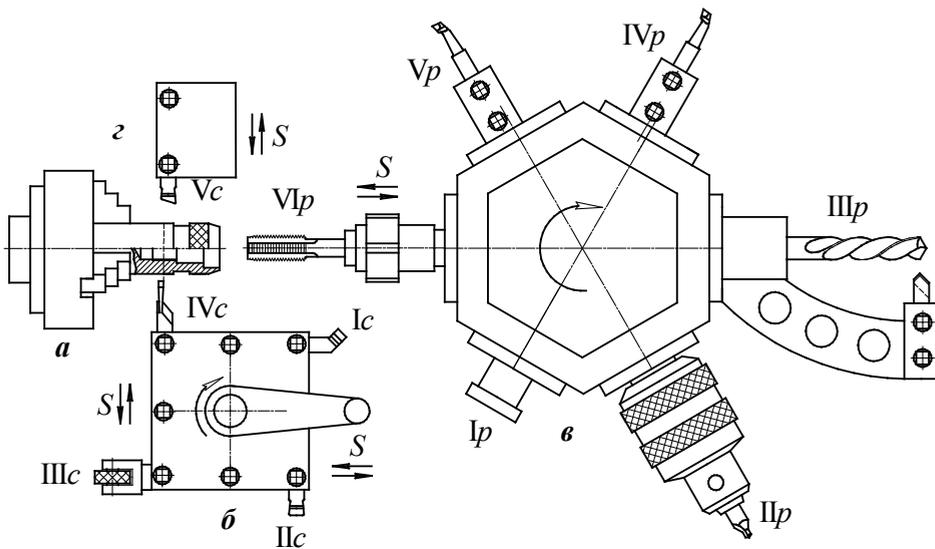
Схема наладки токарно-револьверного станка для обработки втулки:
